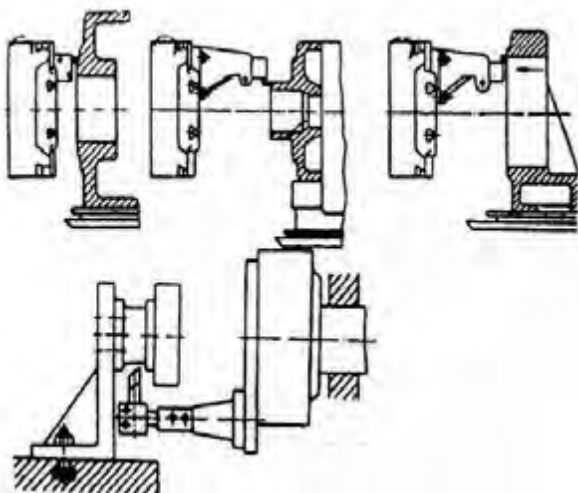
Схеми оброблення різцями на розточувальних верстатах
